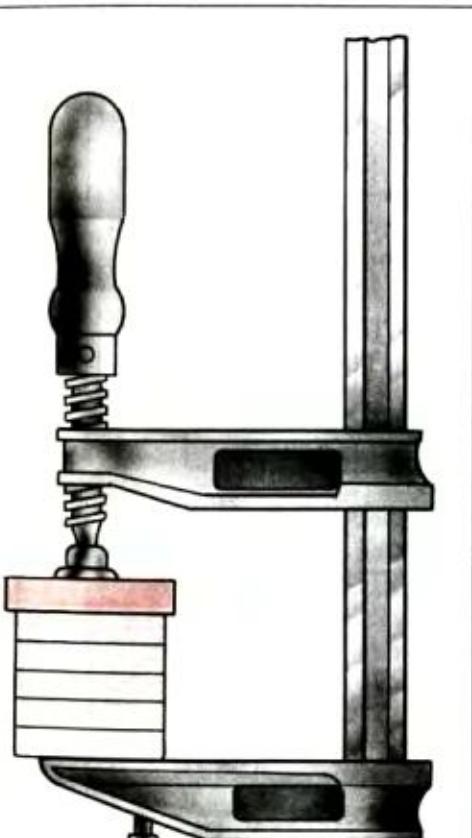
Прессование заготовок столярными винтовыми струбцинами при склейивании заготовок по толщине
